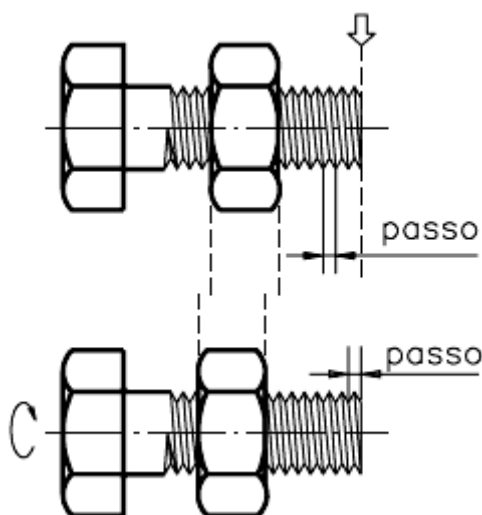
Desenho representativo do parafuso com a porca, o movimento e o passo da rosca.
